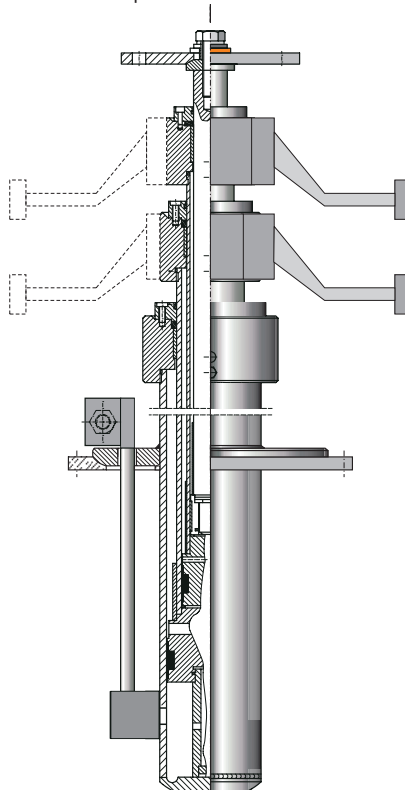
Cilindro telescópico con enganches para brazos de guía
